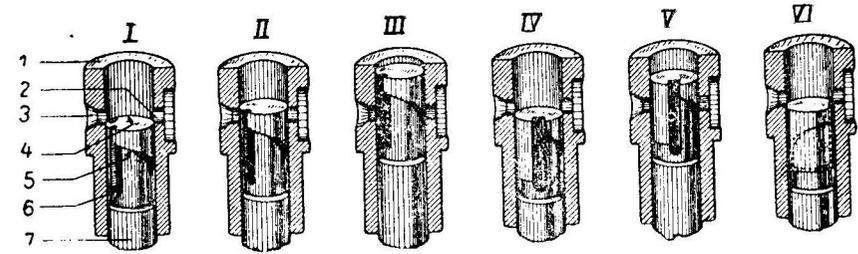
Wirkungsweise der Bosch-Einspritzpumpe
